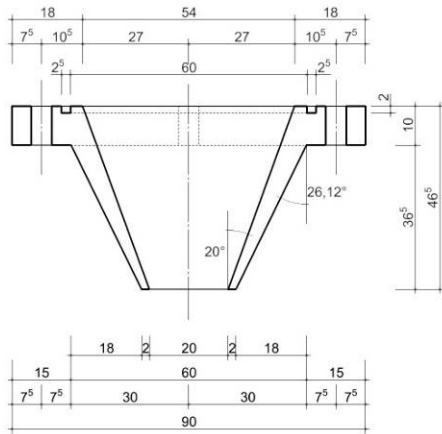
Düse mit 20 mm Öffnungsdurchmesser und 20° Flankenneigung, Werkzeugzeichnung, Vertikalschnitt
